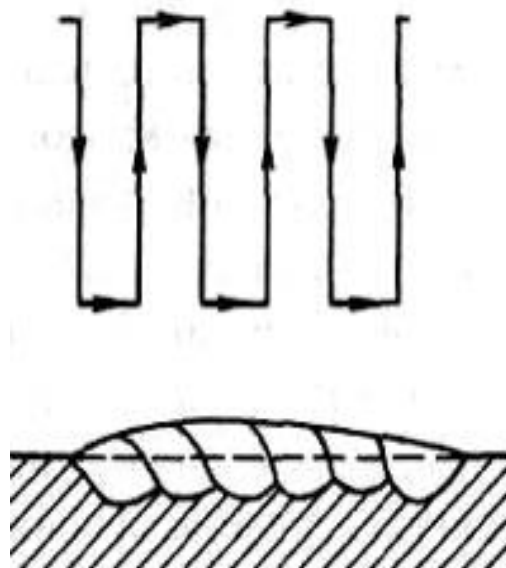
Наплавка плоской поверхности зигзагообразным движением электрода
